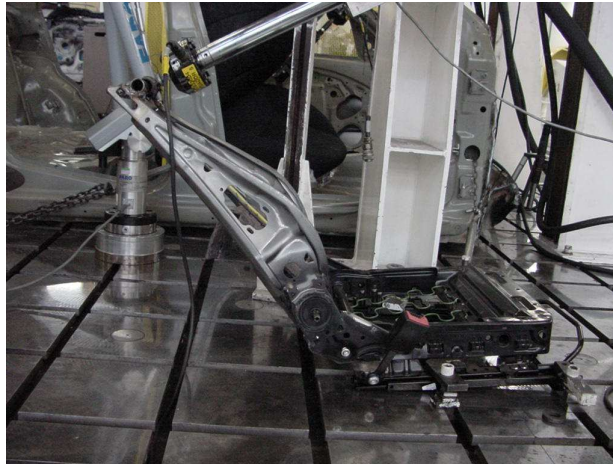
Ensaio de cedimento da estrutura do encosto banco EDC3- Imagem da estrutura após o ensaio
